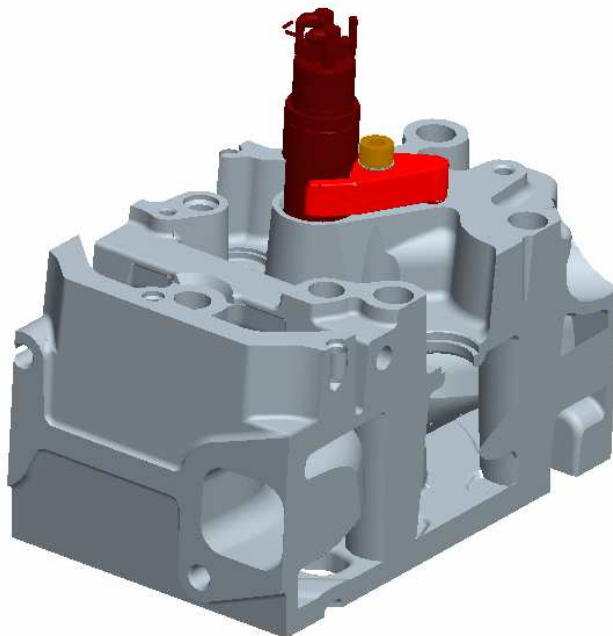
3D model části hlavy motoru s mechanickým vstřikovačem
